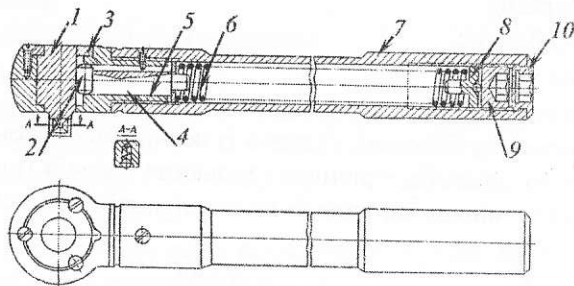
Тарувальний ключ: 1 – кулачок із квадратом; 2 – ролик; 3 – шайба; 4, 8 – упор; 5 – головка; 6 – пружина; 7 – рукоятка; 9 – гайка; 10 – пробка
